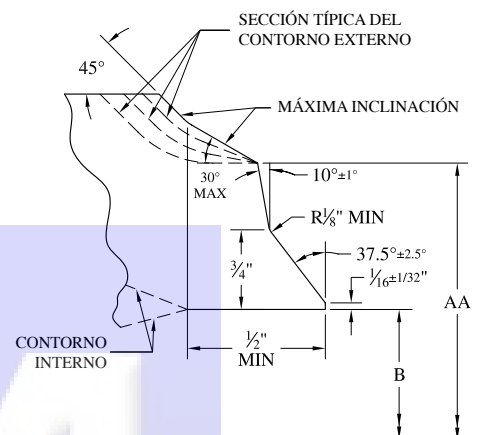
B.- Extremo soldable para ensamblar con arillo de respaldo bipartido para espesores de tubería mayor a "t" 7/8"
